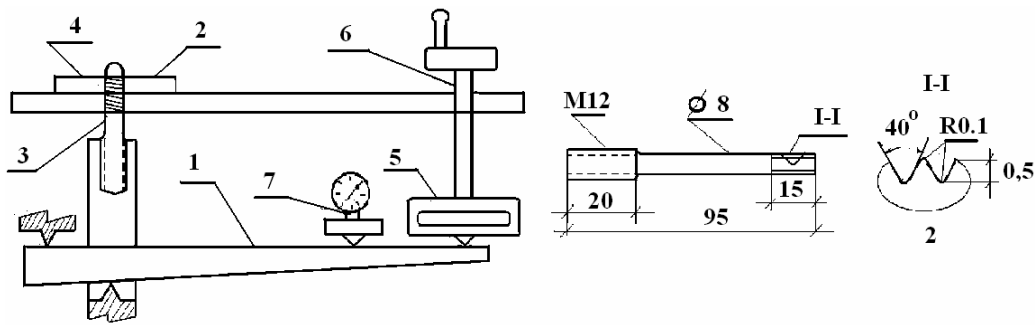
Схема нагружения образца и измерения перемещений по методу «Имплант»: а – установка «Имплант», б – образец «Имплант»; 1 – рычаг, 2 – пластина, 3 – образец-имплант, 4 – сварной шов, 5 – динамометр, 6 – винт нагружения, 7 – стрелочный индикатор перемещений
